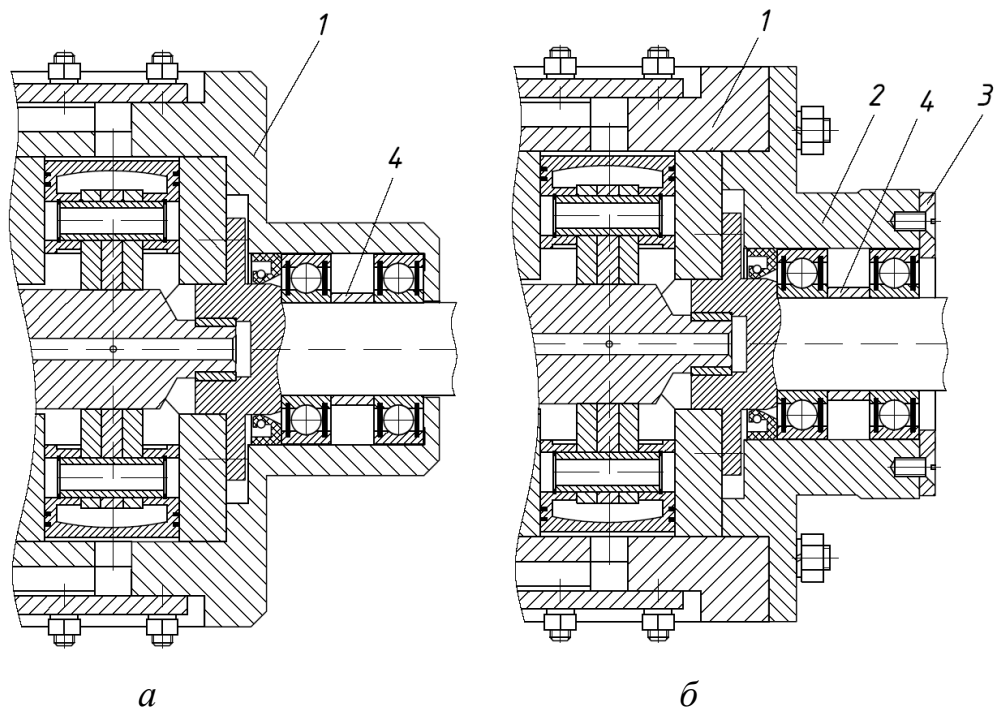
Конструктивні схеми розміщення опорних підшипників центрального ротора: *а* – у корпусі двигуна; *б* – у кришках;
